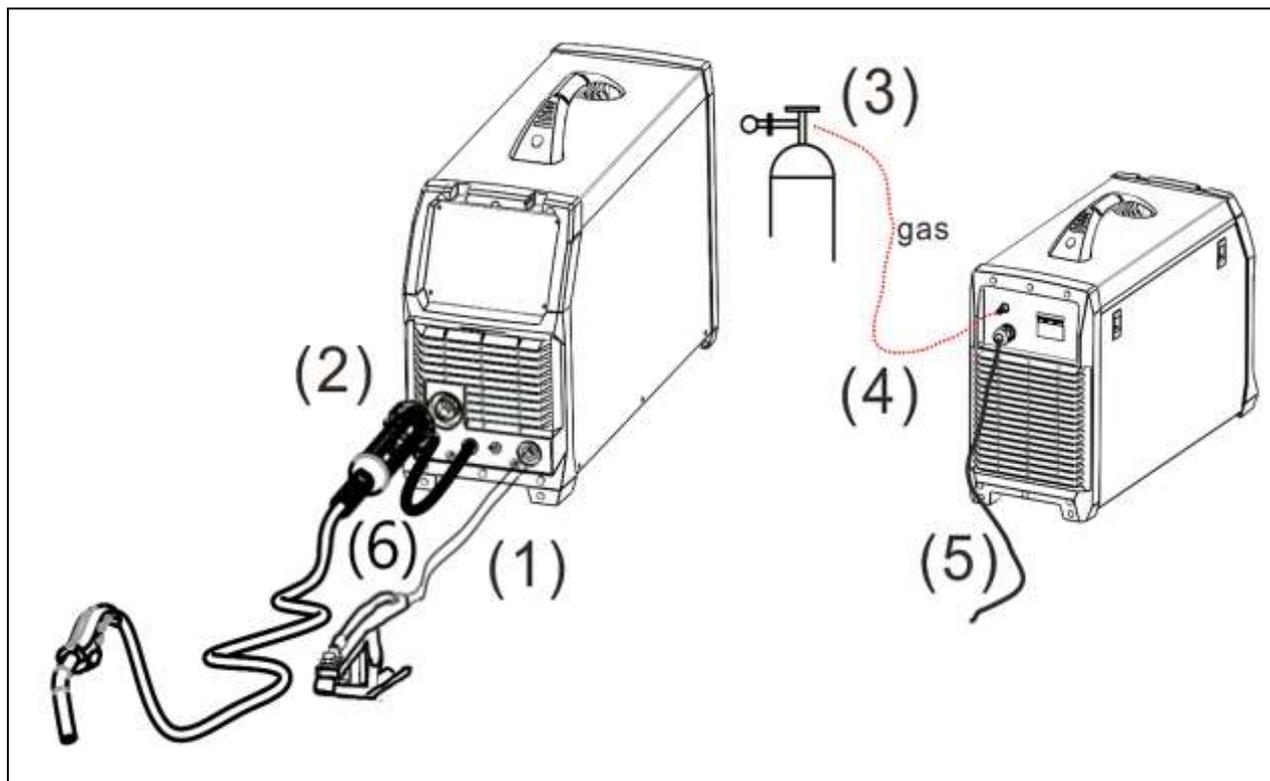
Diagrama conexão soldagem MIG/MAG com gás.
